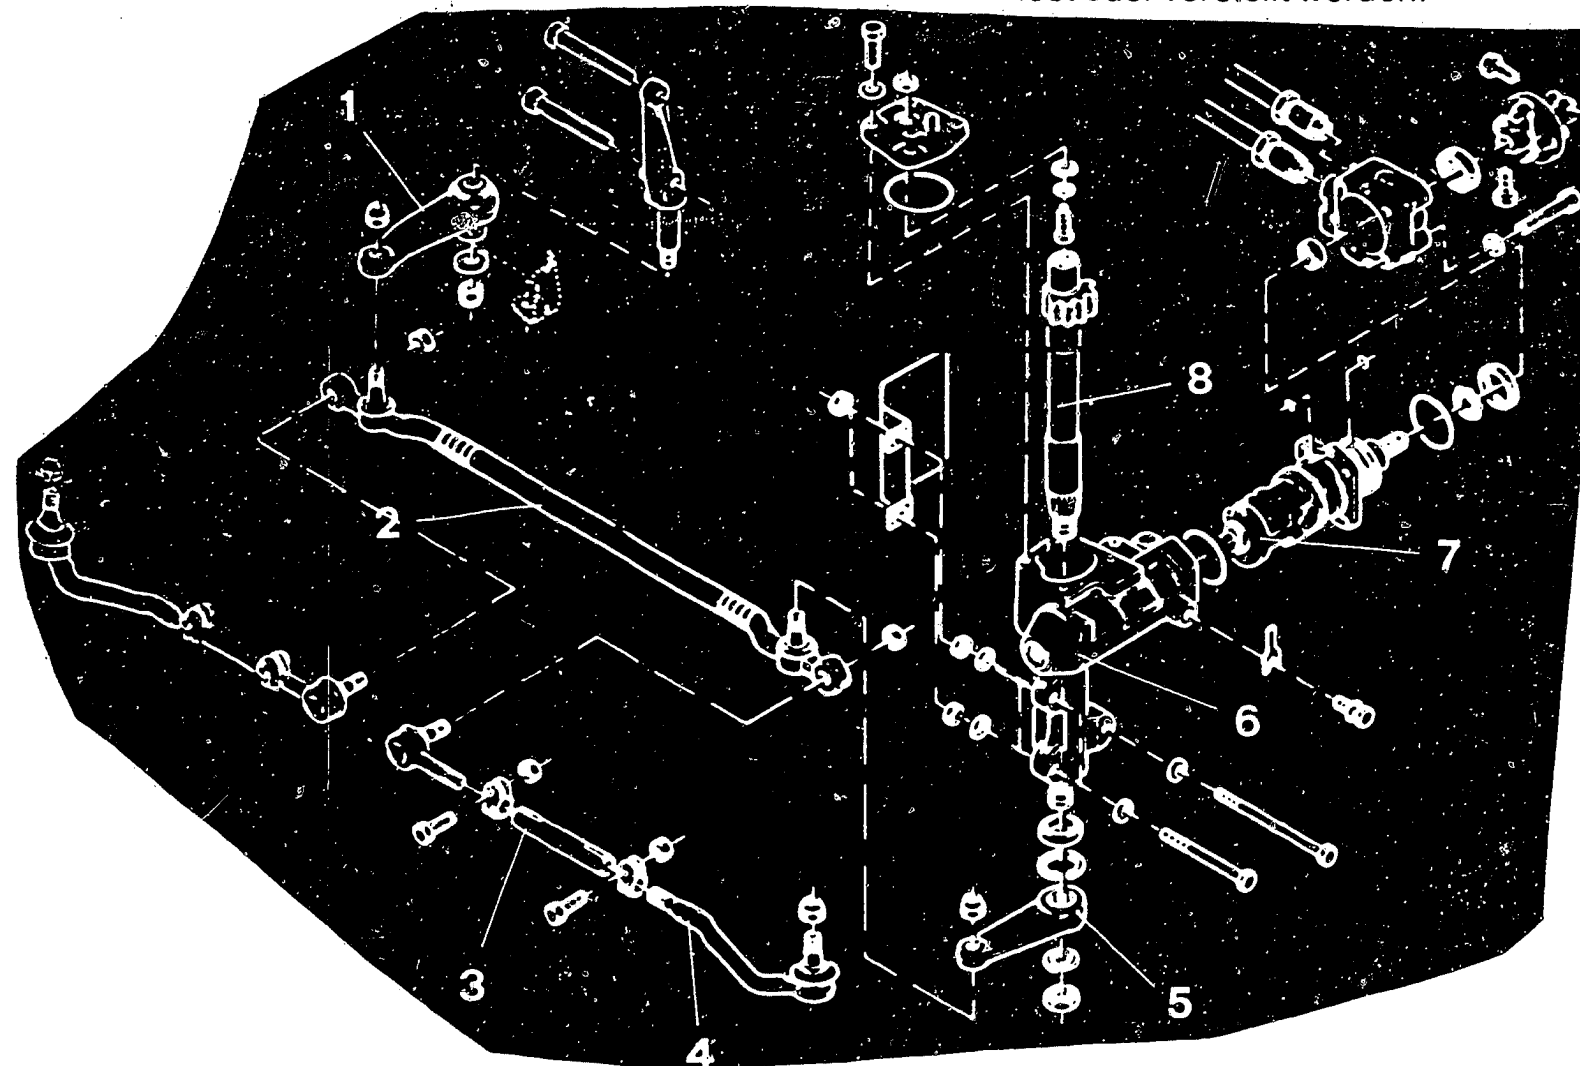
Servoausführung der Kugelumlauf Lenkung. Die wichtigsten Teile sind: 1 Führungshebel – 2 Spurstangen-Mittelstück – 3 Regulierhülse – 4 Gelenkkopf – 5 Lenkstockhebel – 6 Gehäuse – 7 Spindel mit Umlaufkugeln – 8 Segmentwelle.
